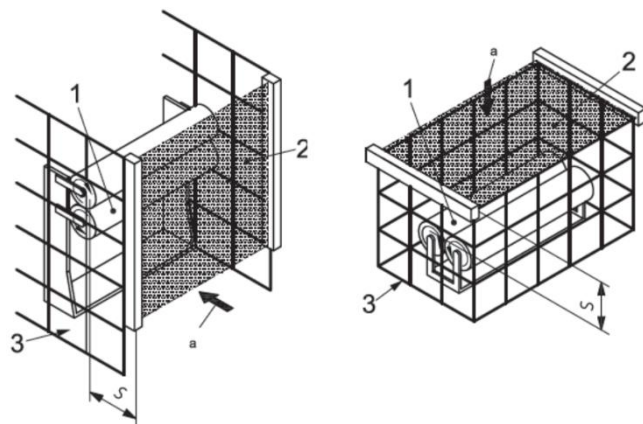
Esempi in cui la zona di rilevamento è ortogonale alla direzione di approccio
